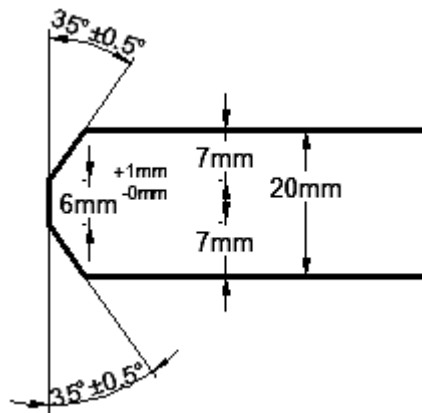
DIMENSIONES Y TOLERANCIA DE BISEL (1)
